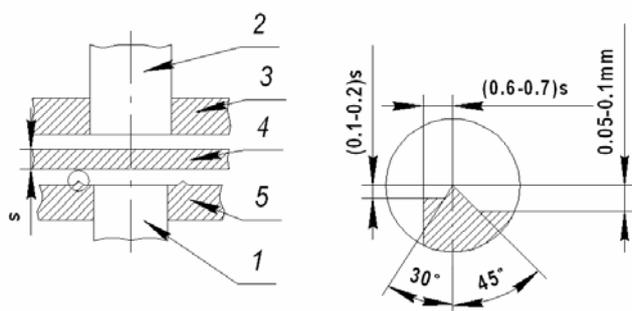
Схема чистовой вырубки со сжатием (1 – пуансон, 2 – выталкиватель, 3 – матрица, 4 – заготовка, 5 – съемник-прижим)
